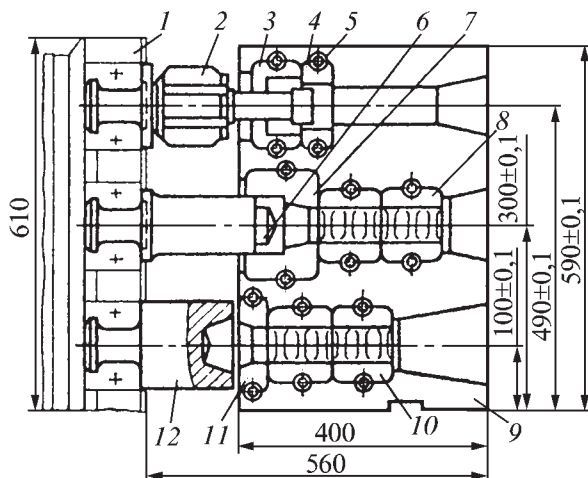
Высачный штамп для поковки типа кольца: 1 — блок пуансонов; 2 — сборный просечной пуансон; 3 и 4 — просечные вставки; 5 — винт для вставок; 6 — формовочный пуансон; 7 — формовочная вставка; 8 и 10 — зажимные вставки; 9 — матрица; 11 — подъемная вставка; 12 — наборный пуансон
